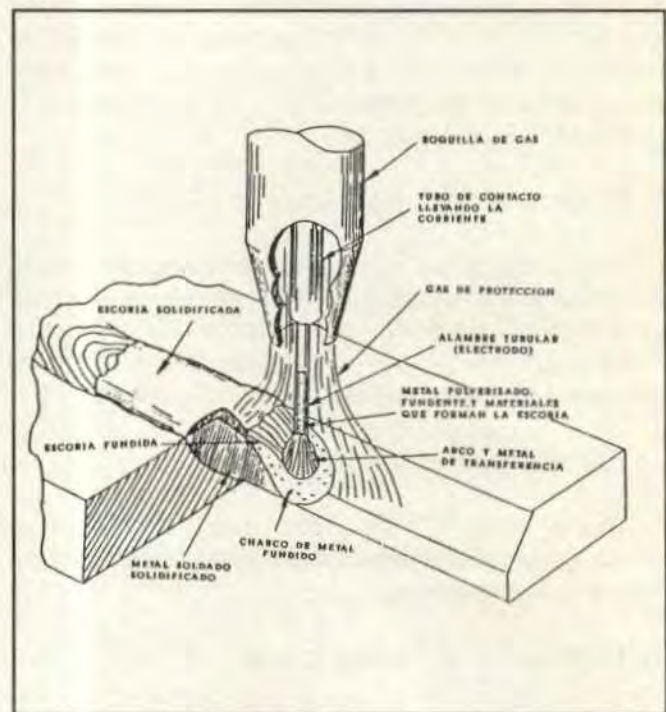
Detalle de la Soldadura F.C.A.W.
